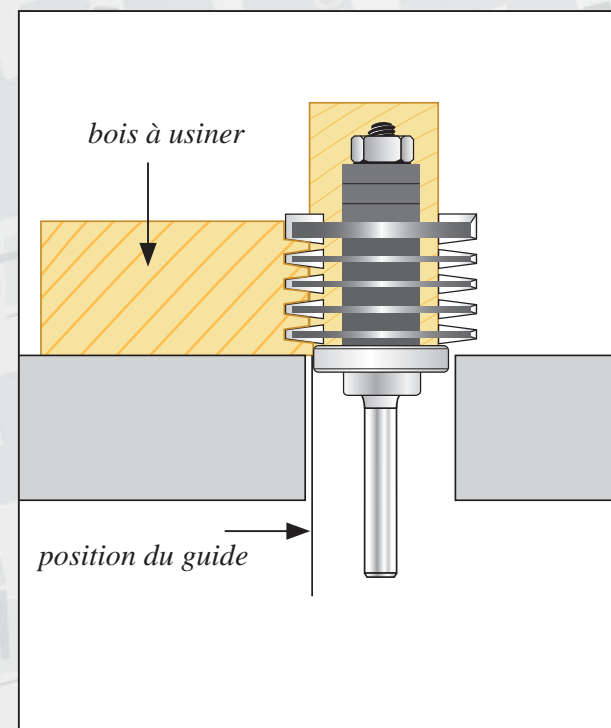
réglage de la largeur de coupe : guide parallèle dans le prolongement du roulement.
